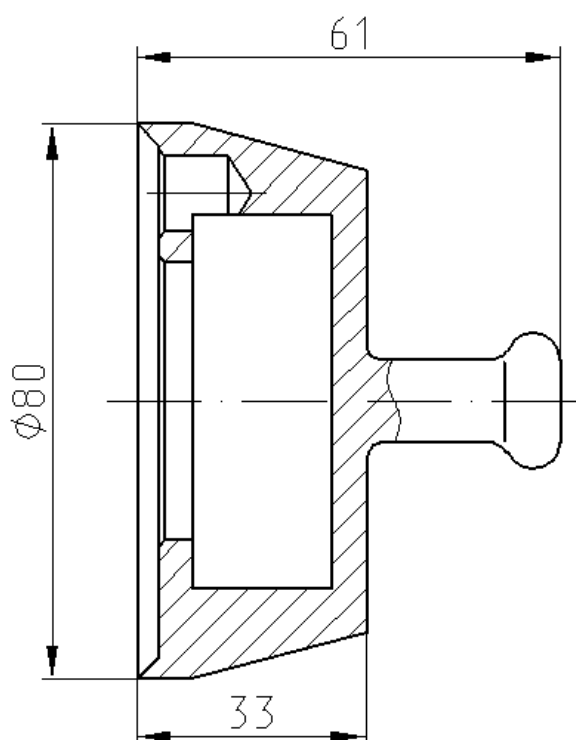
ЗМ 7853-4215 – Оправка для установки сальникодержателя
